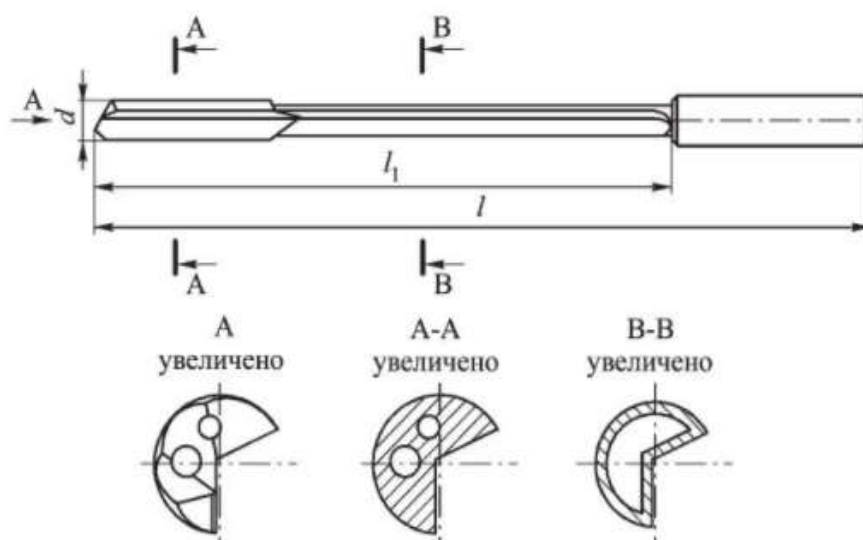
Сечение стержня ружейного сверла (Вид В-В)
